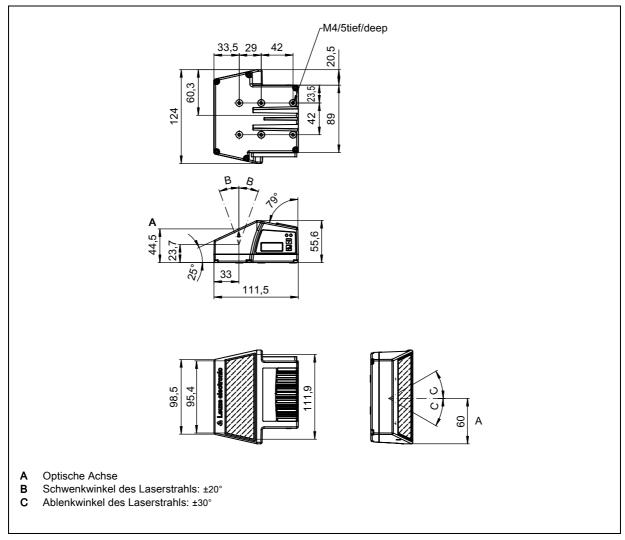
Maßzeichnung Scanner mit Schwenkspiegel BCL 300/\ BCL 301/O...100
